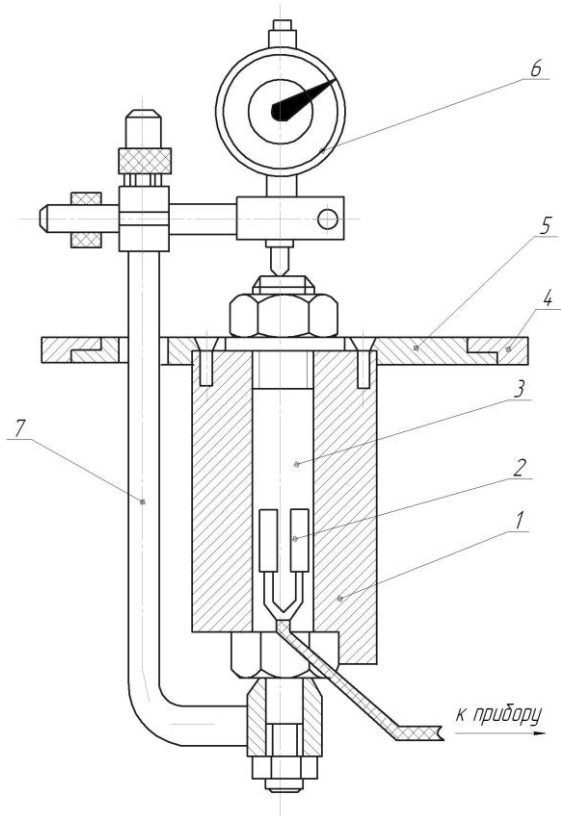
Конструкция приспособления для проведения лабораторной работы
